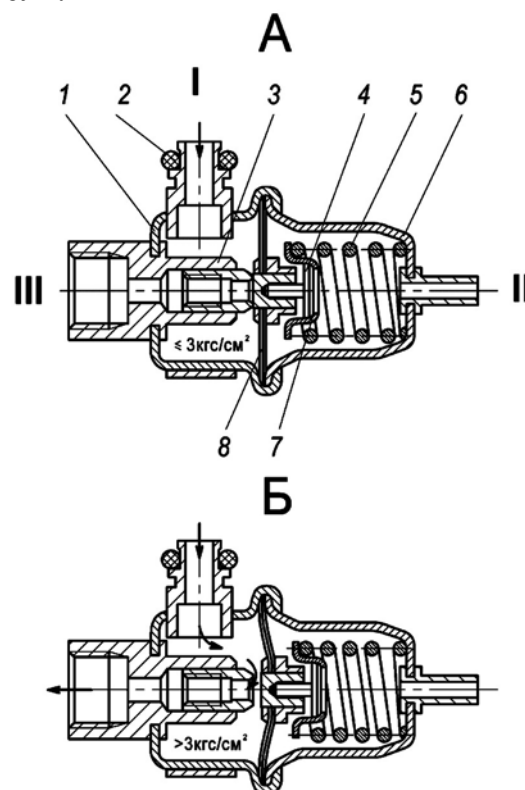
Регулятор давления топлива: 1 - корпус; 2 - резиновое кольцо; 3 - седло клапана; 4 - упор; 5 - пружина; 6 - крышка; 7 - тарелка пружины; 8 - диафрагма с клапаном; А - клапан закрыт; Б - клапан открыт; I -от топливопровода двигателя; II - к ресиверу; III - к топливному баку
